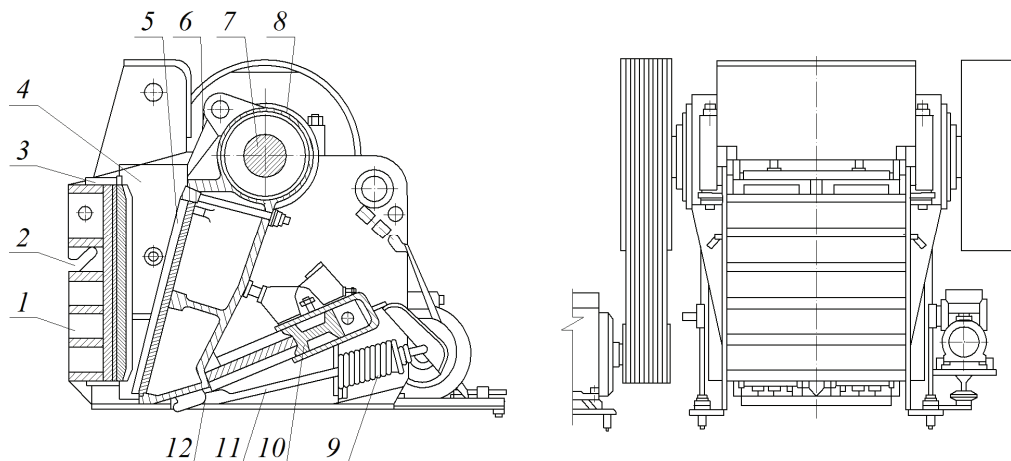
Общий вид дробилок моделей СМД-108 и СМД-109: 1 – станина; 2 – неподвижная дробящая плита; 3 – упоры; 4 – боковые футеровки; 5 – подвижная дробящая плита; 6 – шток; 7 – эксцентриковый вал; 8 – подвижная щека; 9 – пружина; 10 – механизм регулирования выходной щели; 11 – тяга; 12 – сменный сухарь;
